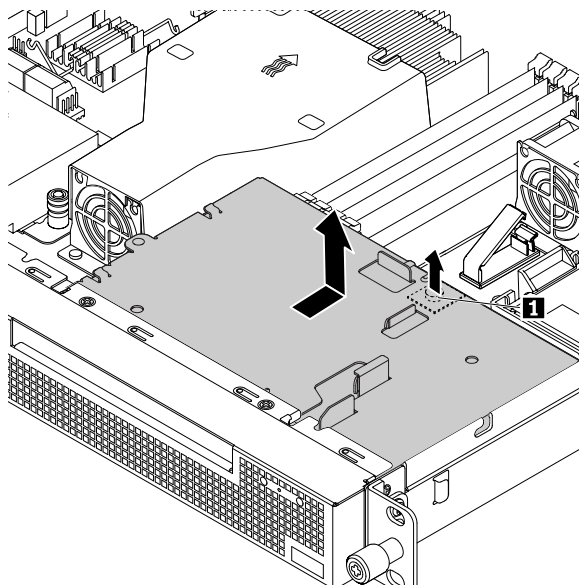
Halterung für das flache optische Laufwerk entfernen
